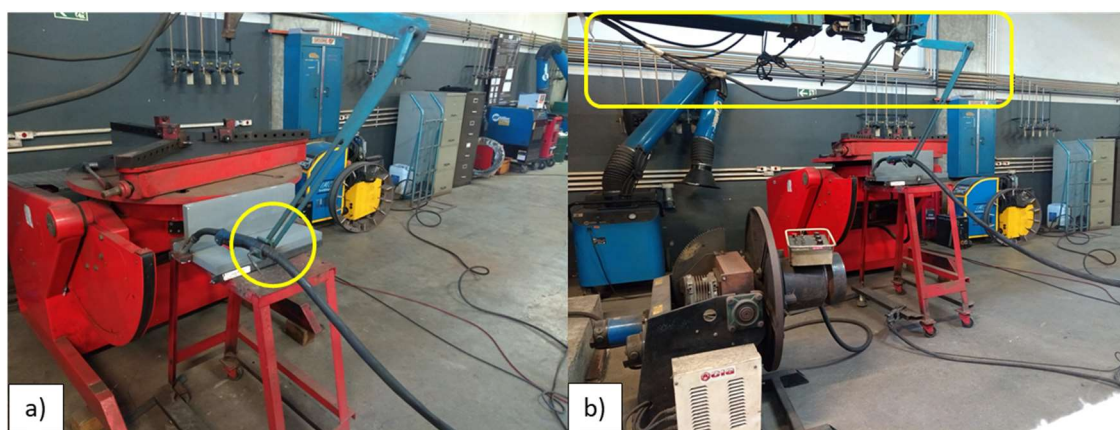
(a) arranjo de soldagem, com destaque para posicionamento da tocha no suporte; (b) fotografia mais ampla, destacando o sistema do braço mecânico na parte superior da imagem.
